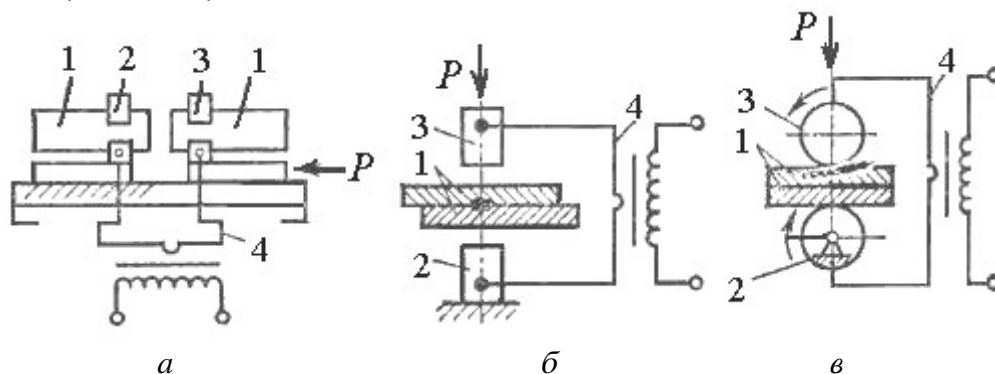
Схемы контактной сварки: *а* – стыковой: 1 – заготовки, 2 – неподвижный токоподвод, 3 – подвижный токоподвод, 4 – сварочный трансформатор; *б* – точечной: 1 – заготовки, 2 – неподвижный электрод, 3 – подвижный электрод, 4 – трансформатор; *в* – шовной: 1 – заготовки, 2 – неподвижный ролик-электрод, 3 – подвижный ролик-электрод, 4 – трансформатор
